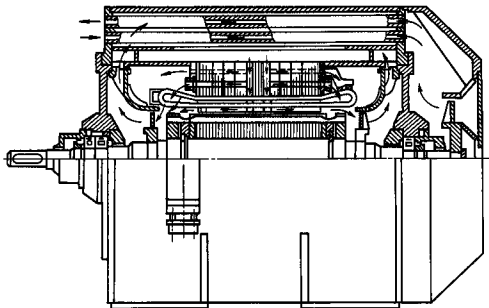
Продольный разрез двигателя 2АЗМВ1 Стрелками указано направление движения охлаждающего воздуха (два контура)
